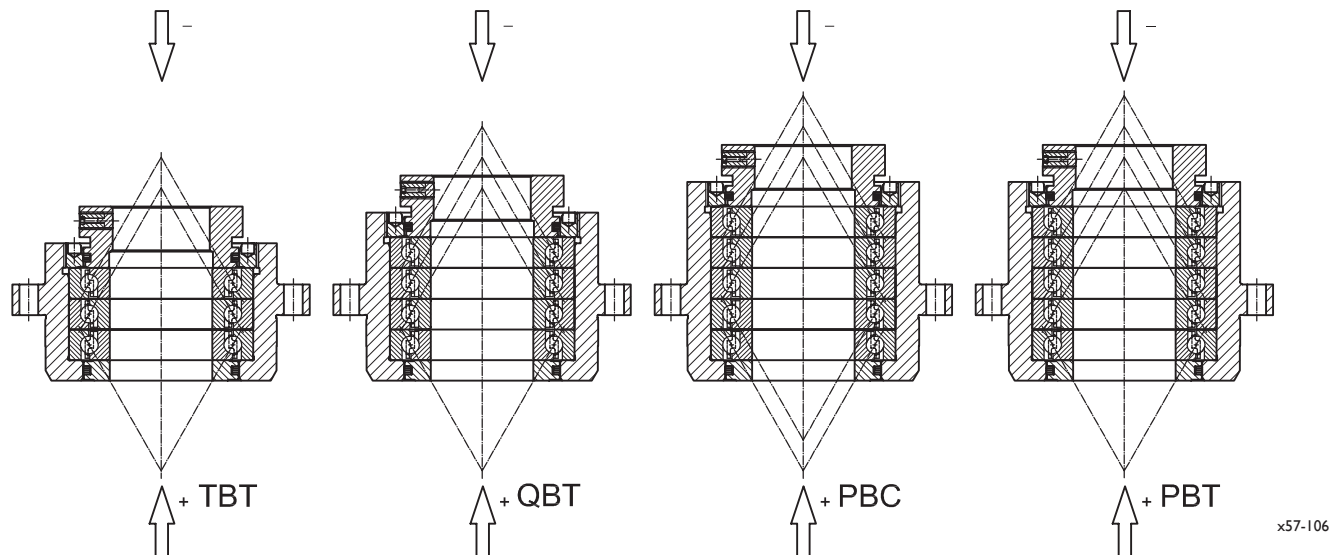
Asymmetrische Lageranordnungen für überwiegend einseitig belastete Kugelgewindetriebe
